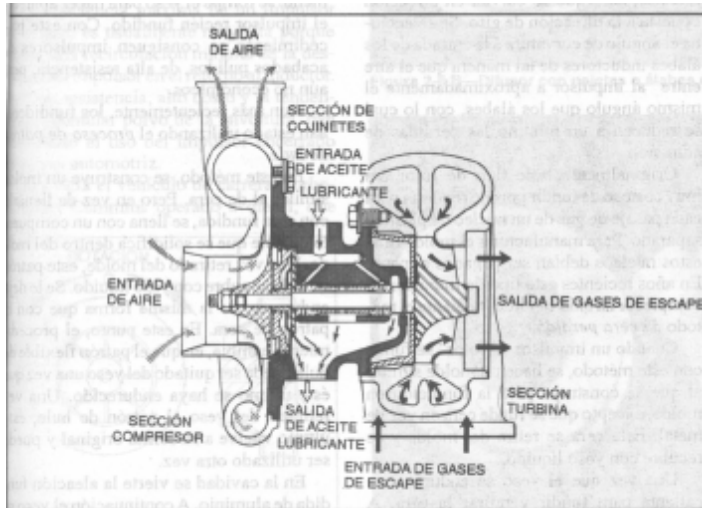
Sección recta de un turbocargador típico. Dibujo cortesía de Schwitzer.
